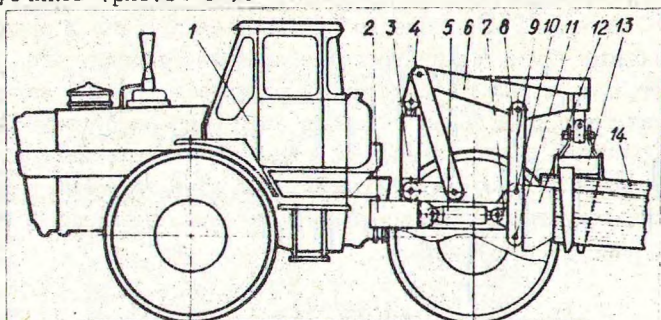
Трелевочная машина с увеличенной зоной действия захвата: 1-трактор; 2-рама; 3, 5-гидроцилиндры; 4-рычаг; 6-стрела; 7-нижнее звено; 8-верхнее звено; 9-задний рычаг; 10, 11-шарниры; 12-щит; 13-захват; 14-пачка деревьев.
